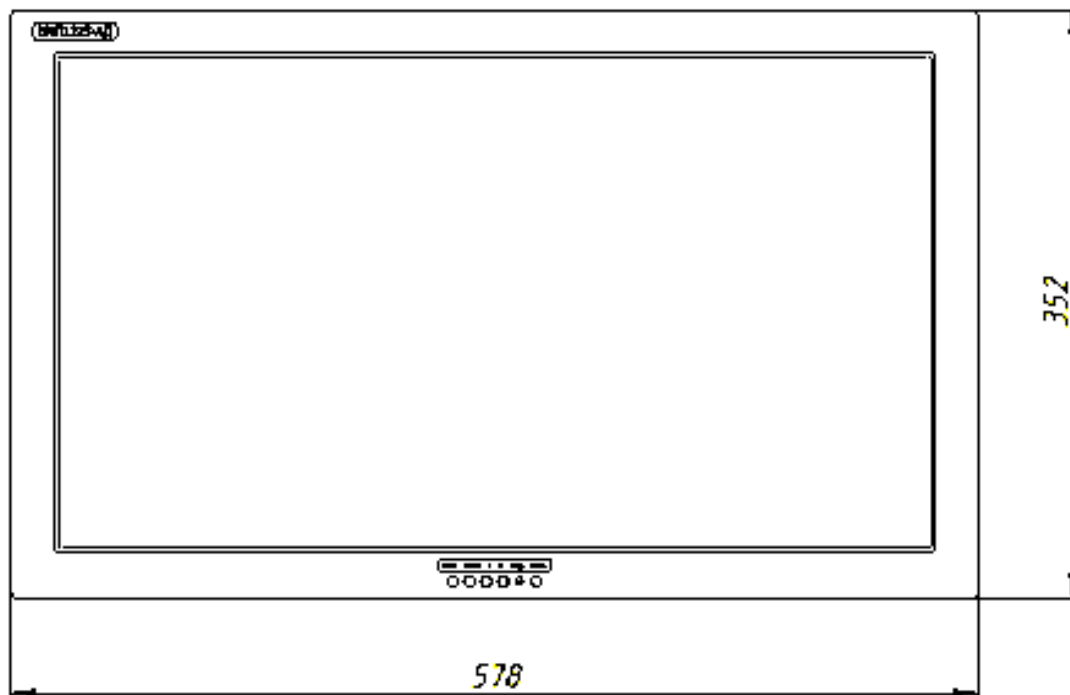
д – Габаритный чертёж лицевой части видеомонитора в исполнении ВМП1225-АД-5-Х-Х-Х
